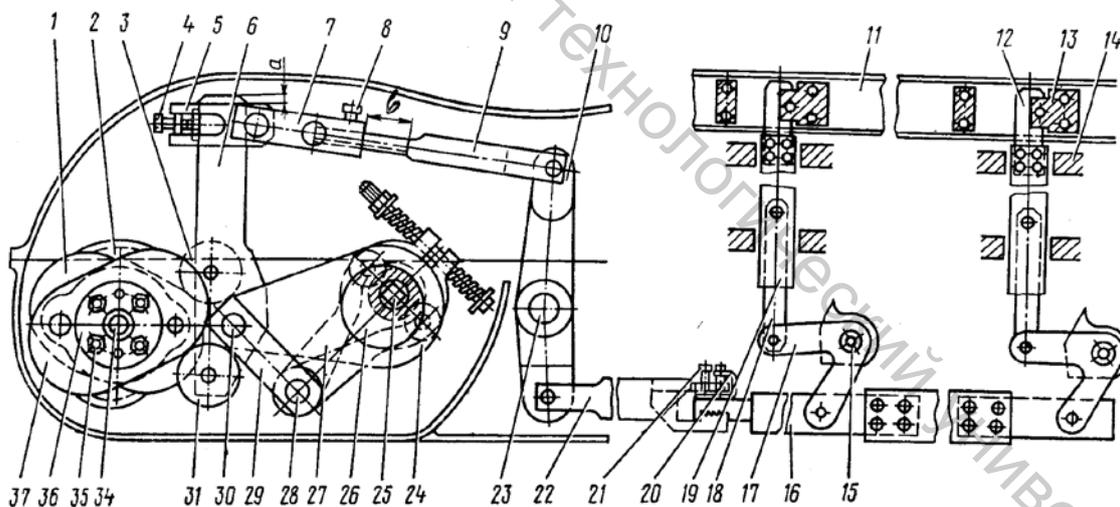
Устройство для передачи движения ремизным рамам и отвода рычага
